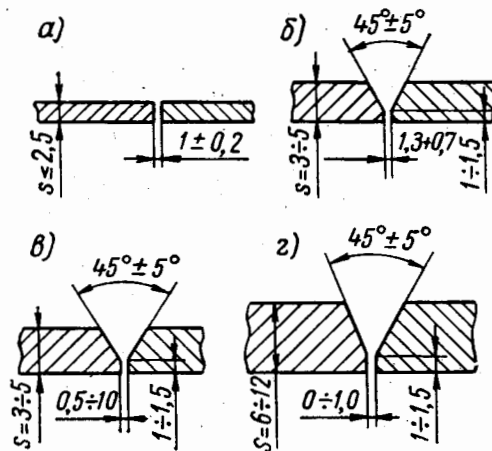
Конструктивные элементы подготовки кромок листовой стали марки 0X23H28M3Д3T, свариваемой полуавтоматической и автоматической аргоно-дуговой сваркой: а — без разделки кромок и б — V-образная разделка кромок при полуавтоматической сварке; в и г — V-образная разделка кромок при автоматической сварке
